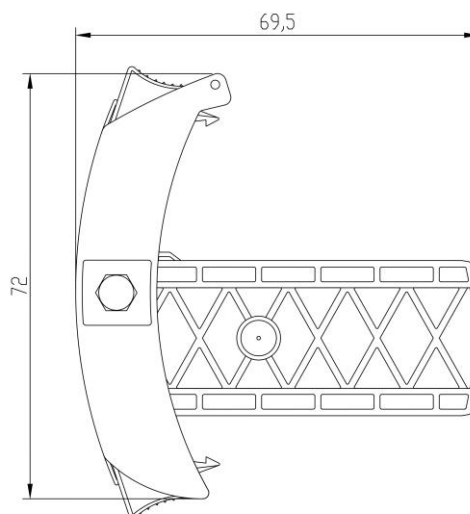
Общий вид рабочей крышки ЭПРК. Вид сбоку.
